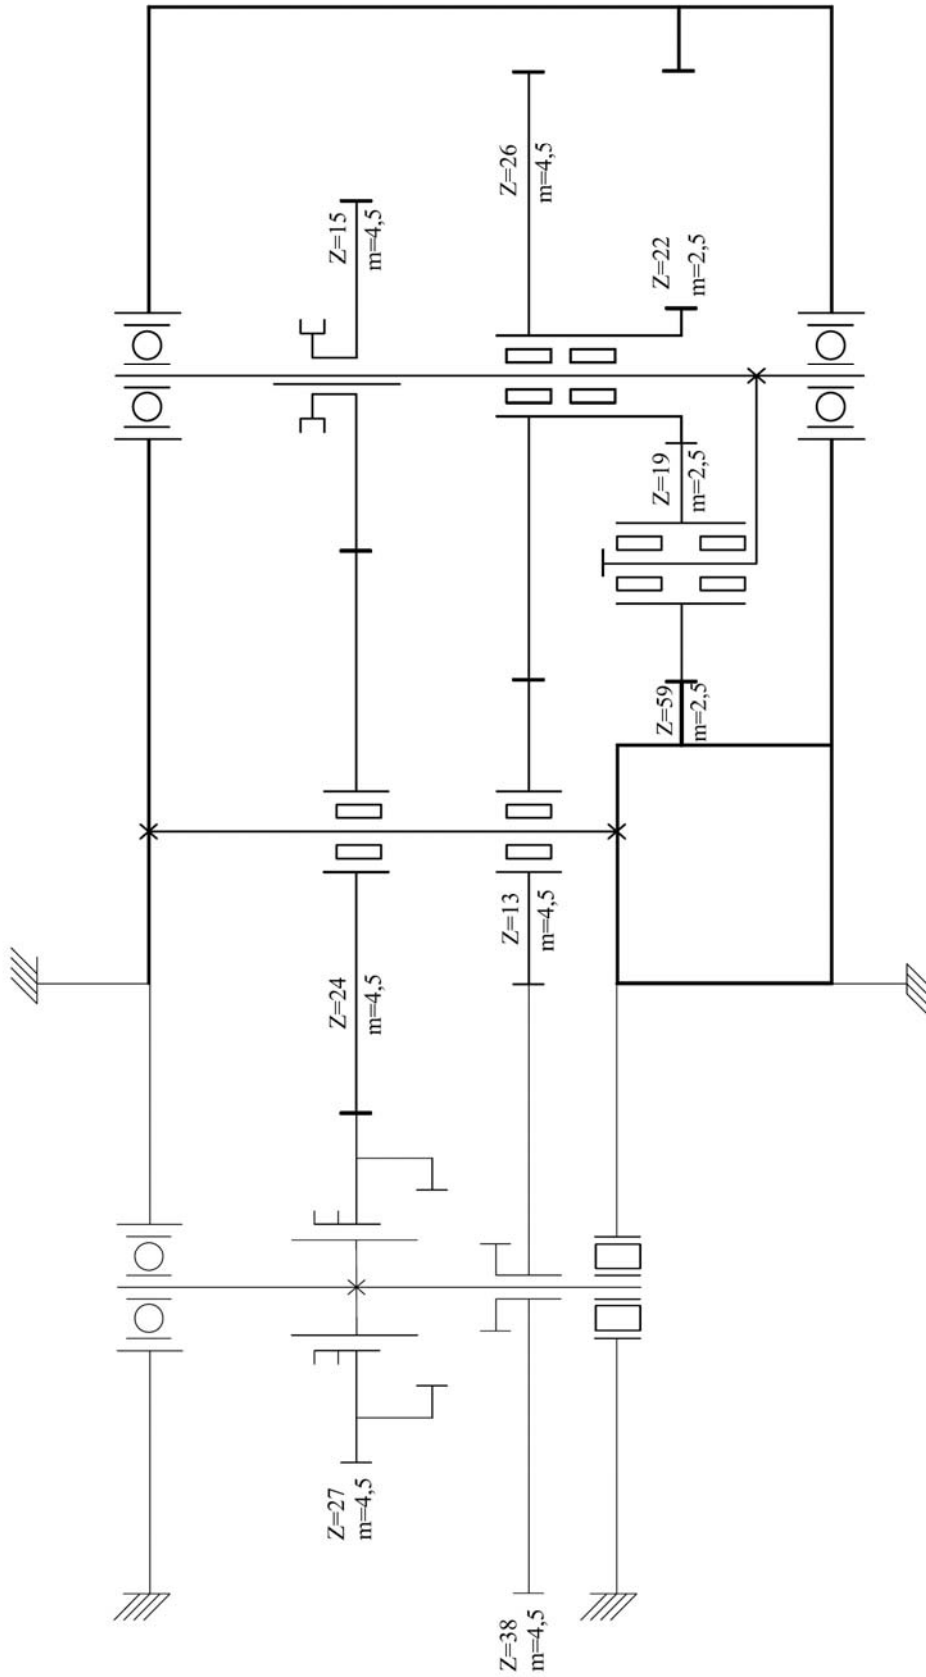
Схема кинематическая ходоуменьшителя тракторов Беларус-1025/1221/1523.
